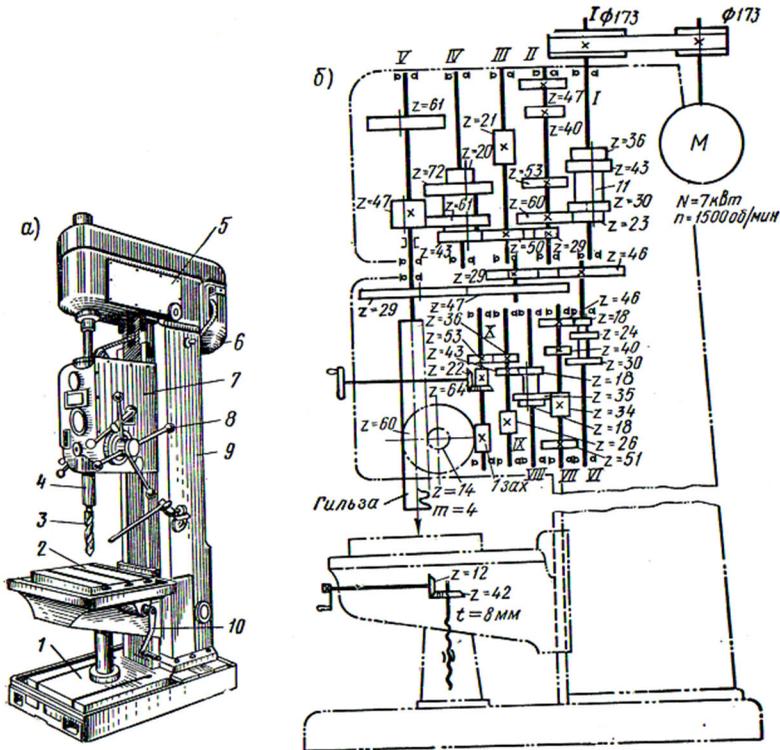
Одношпиндельный вертикально-сверлильный станок модели 2А150: а – общий вид; б – кинематическая схема
